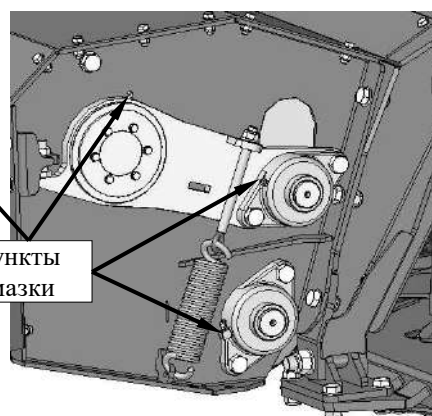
б. Точки смазки самоустанавливающего подшипника смазкой ŁT43
